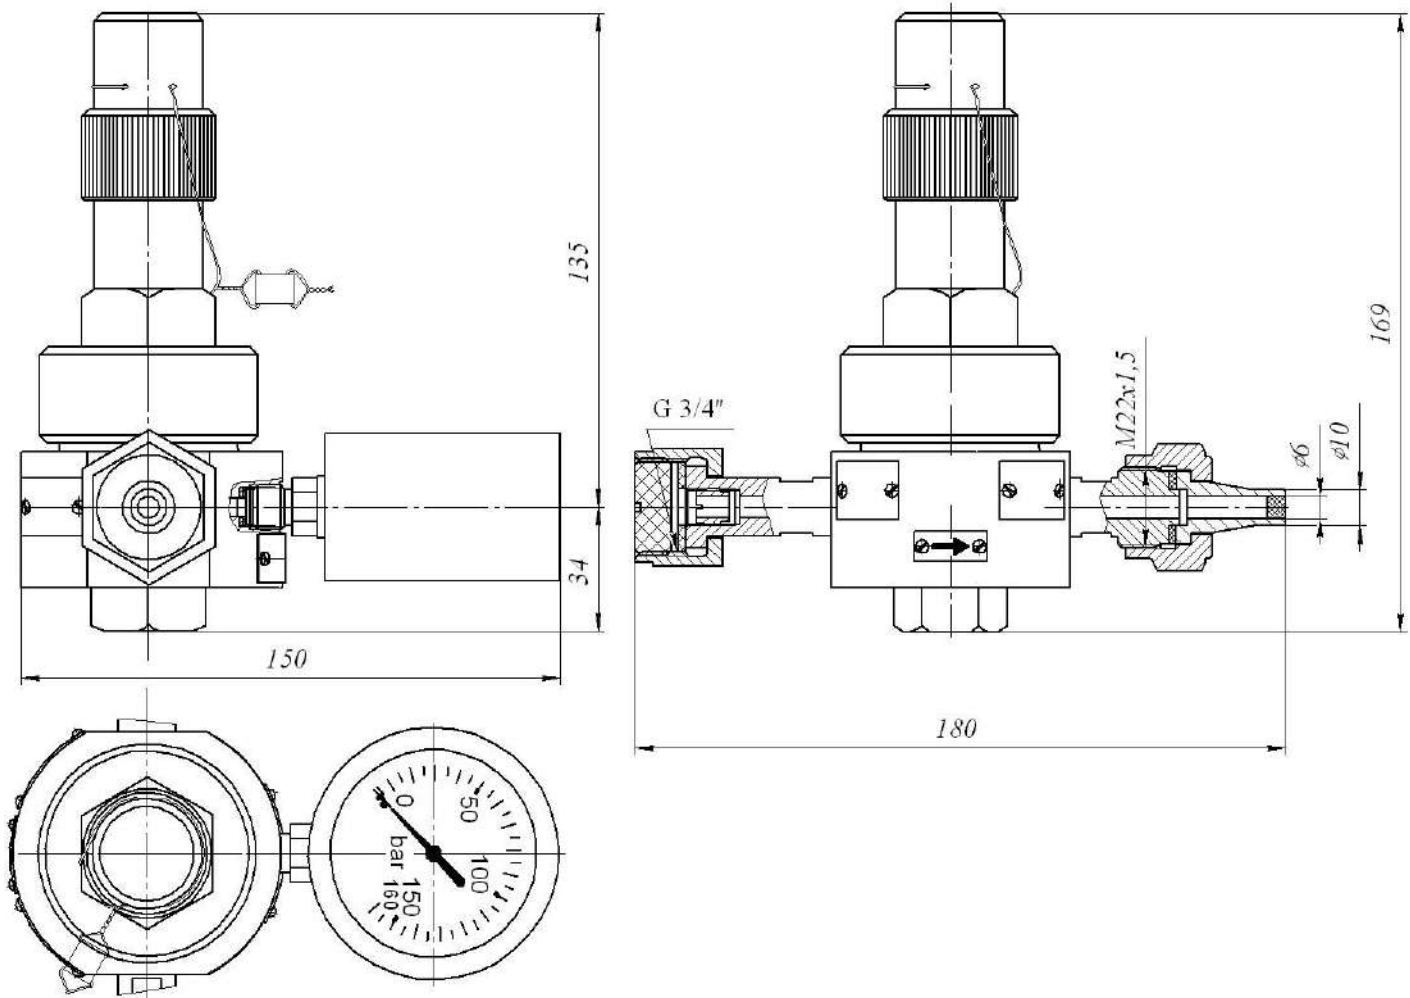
Габаритные и присоединительные размеры РДФ-7-12
